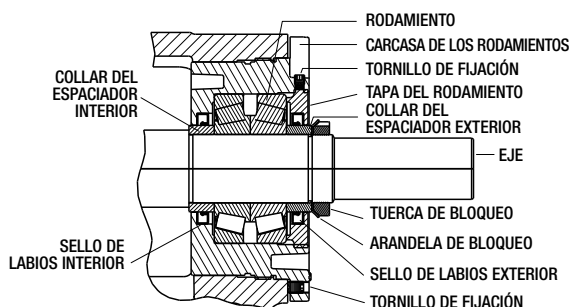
FIGURA H – ENSAMBLAJE DE LA CARCASA DE LOS RODAMIENTOS PARA G1-133 a G1-222
